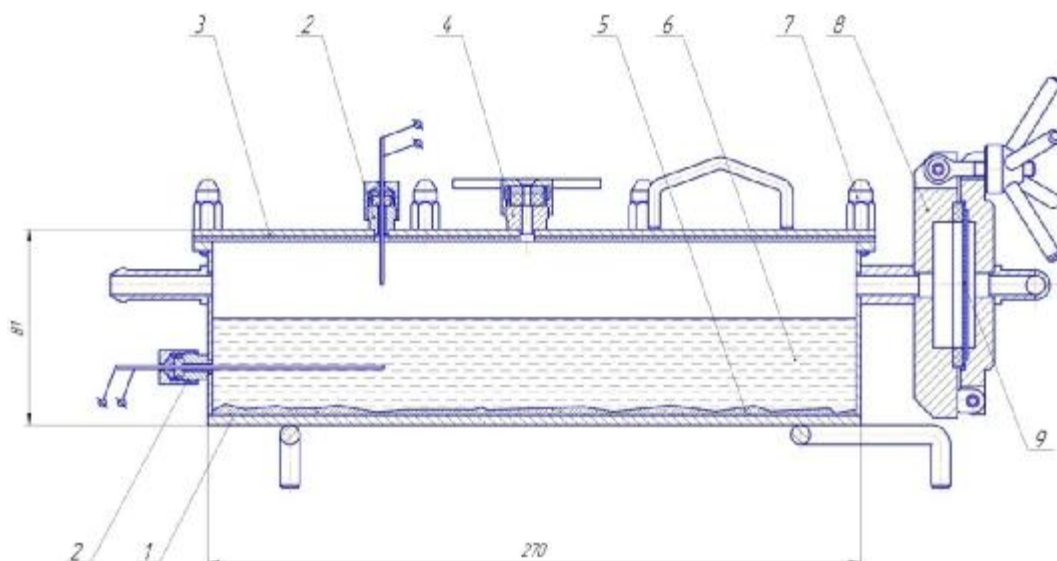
Схема устройства выдержки: 1 – корпус; 2 – разъем ТЭП; 3 – крышка; 4 – разъем для пробоотбора; 5 – образец продуктов резки; 6 – раствор РВ; 7 – прижимная гайка; 8 – фильтродержатель; 9 – фильтр.
